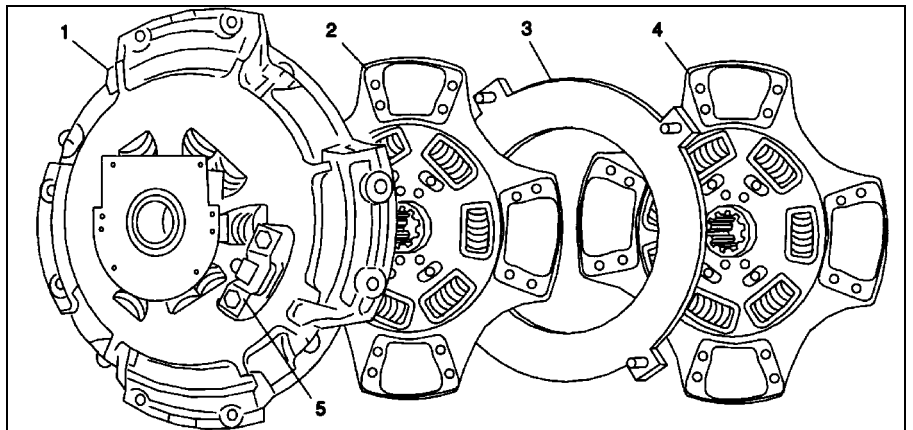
Сцепление Easy-Pedal. 1 - корзина сцепления, 2 - задний ведомый диск, 3 - промежуточный диск, 4 - передний ведомый диск, 5 - механизм регулировки.
